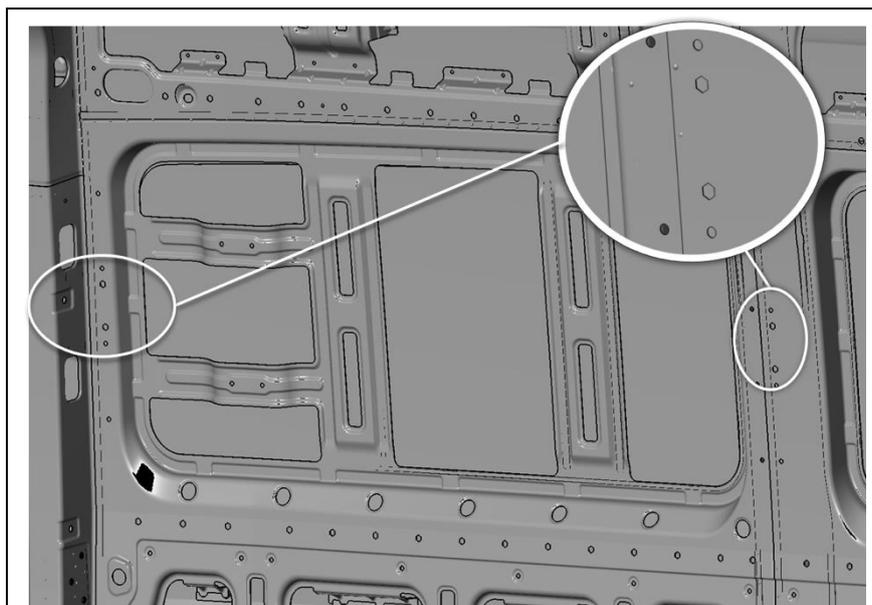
Prééquipement d'étagères sur la carrosserie (panneau latéral), exemple : rail Airliner monté sur le panneau latéral
